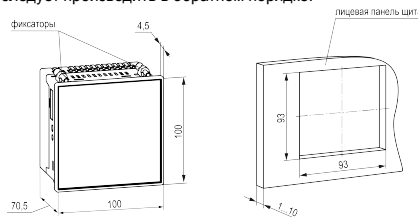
Габаритные размеры и монтажного отверстия в щите
